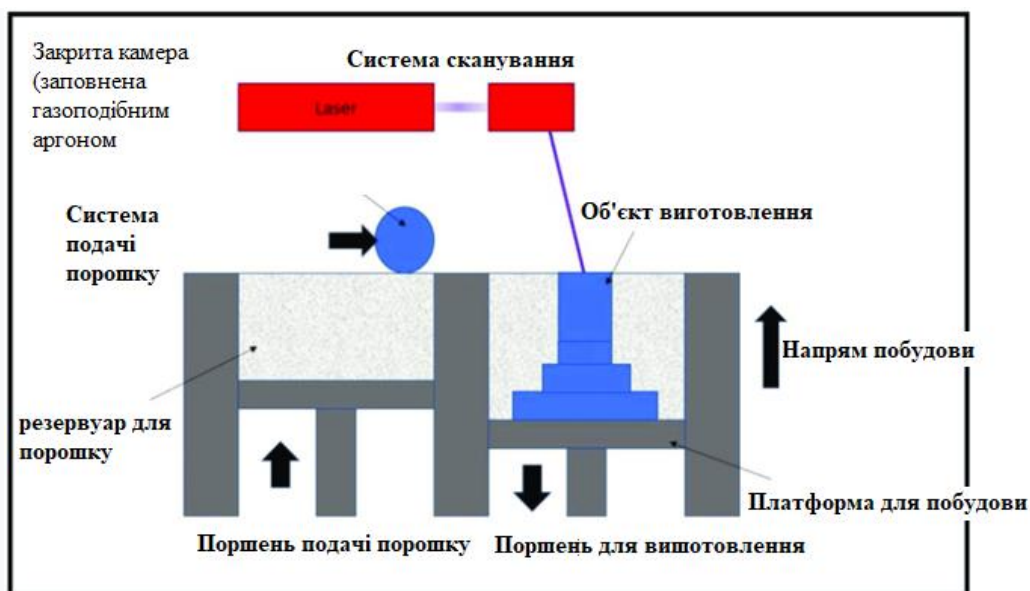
Принципова схема процесу селективного лазерного плавлення (SLM)
